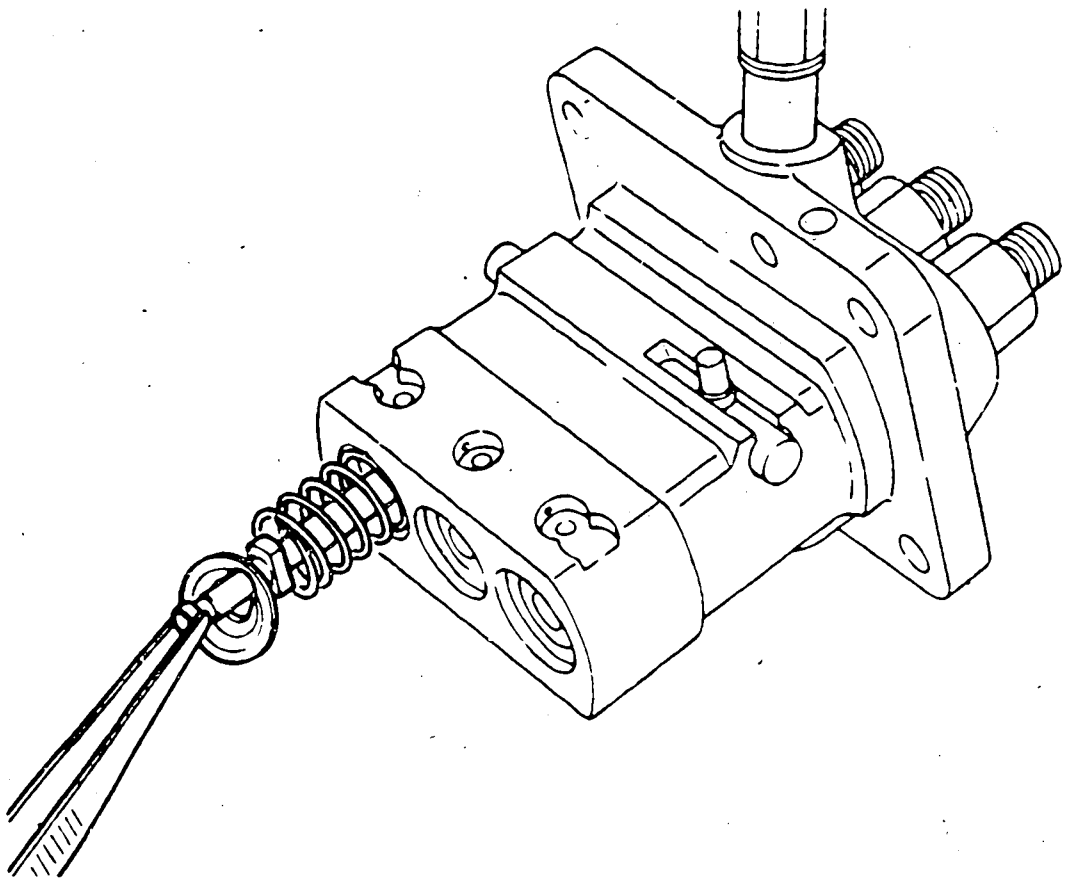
Pumpenkolben, Federteller und Kolbenfeder herausziehen
